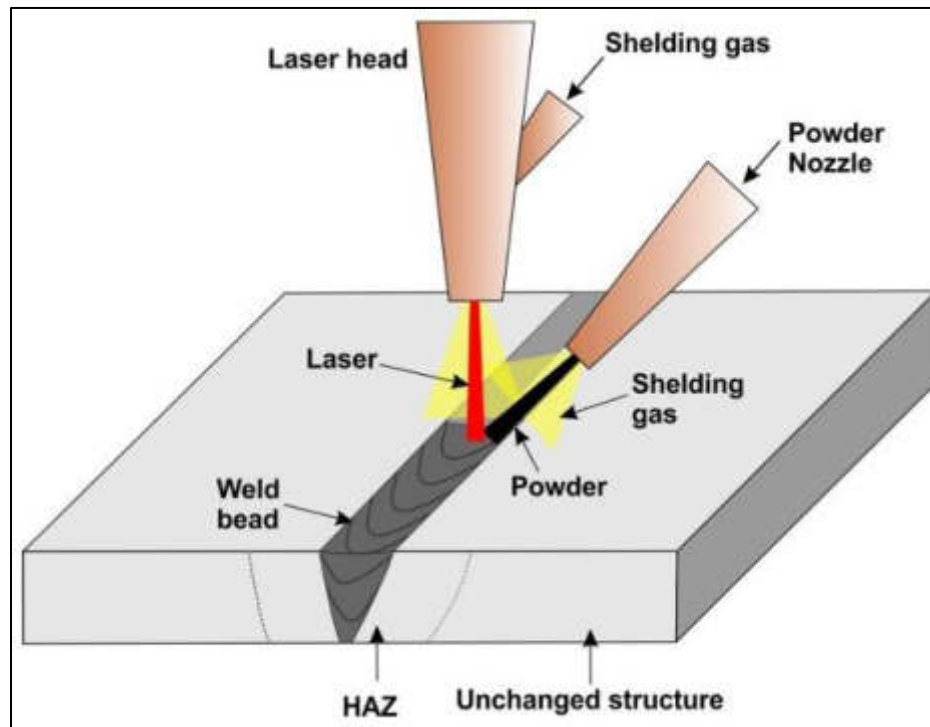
Esquema del proceso de soldadura láser [5]
